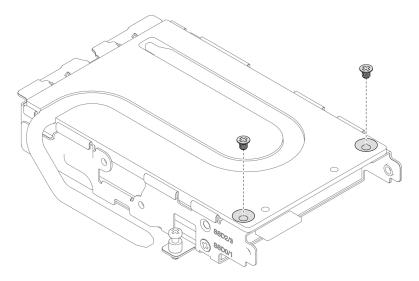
Entfernen der Schrauben vom Kühlkörper
